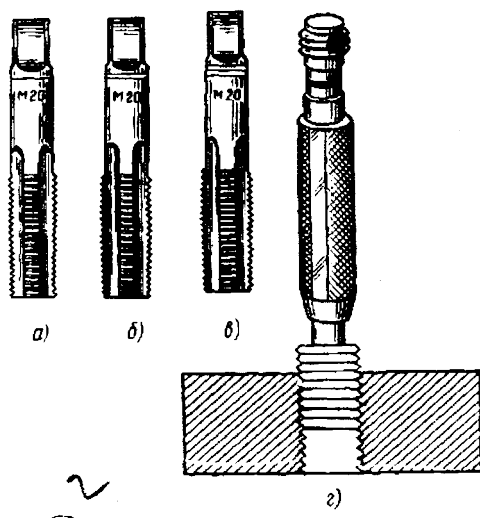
Черновой (*а*), средний (*б*) и чистовой (*в*) метчики и проверка резьбы резьбовым калибром (*г*)
